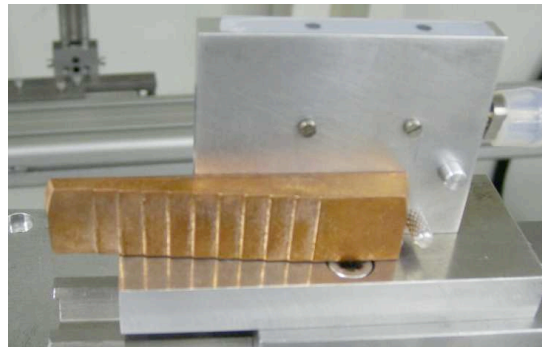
Echantillon Cu 805.23 après sa découpe
